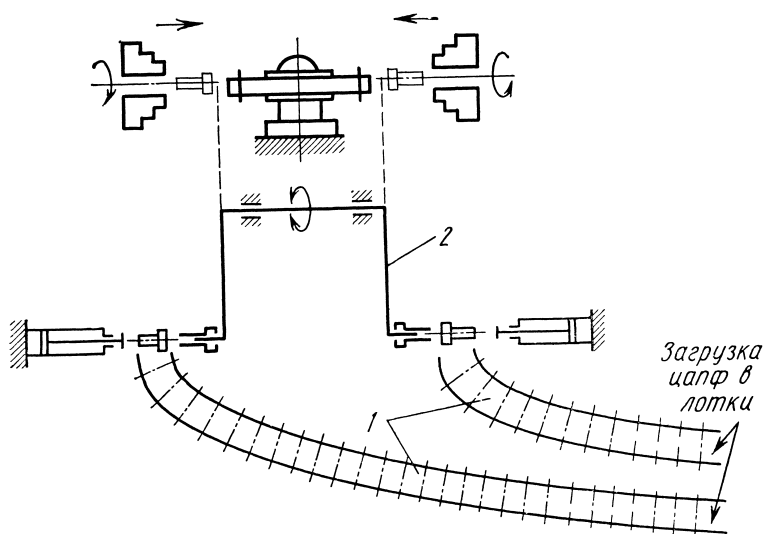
Схема автоматической установки для сборки и сварки балки картера с цапфами
